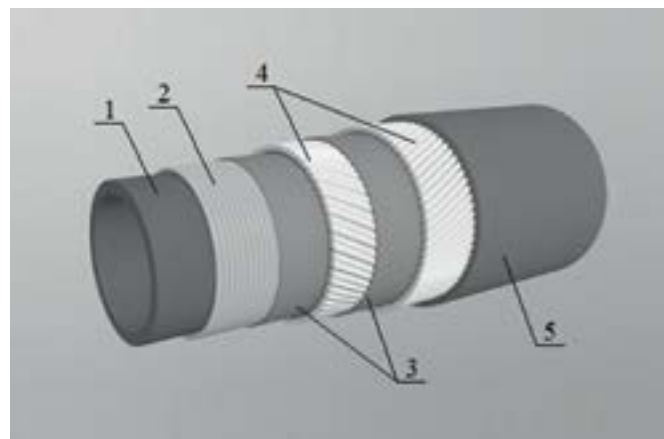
Общий вид армированной металлополимерной трубы с проволочным каркасом:
